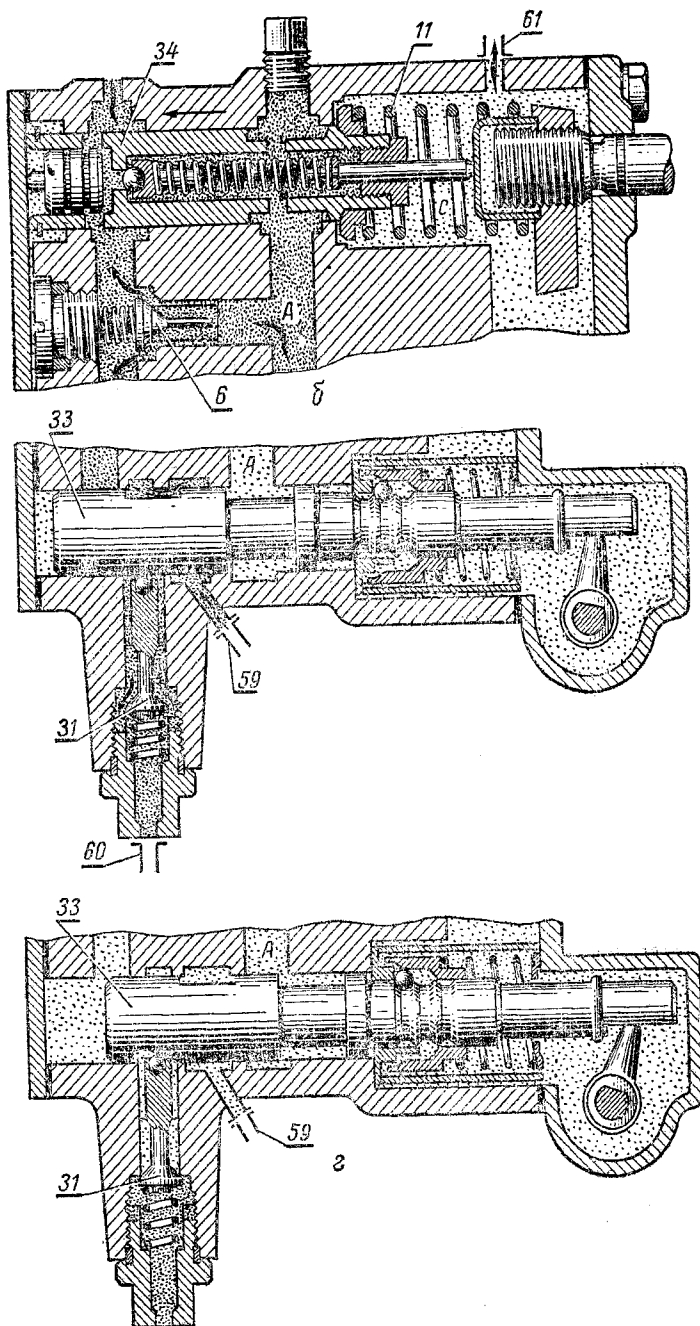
Схема работы гидроувеличителя снепного веса (продолжение):
